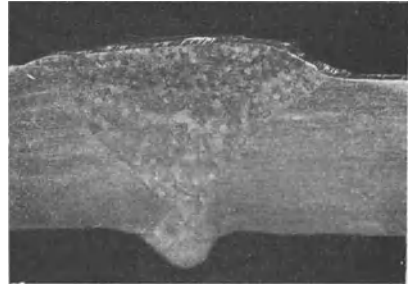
Makroschliff einer Arcatom-Messingdickblechschweißnaht.
